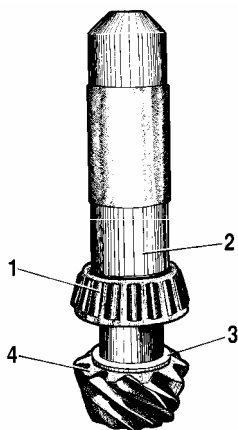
Установка внутреннего кольца заднего подшипника на ведущую шестерню:
